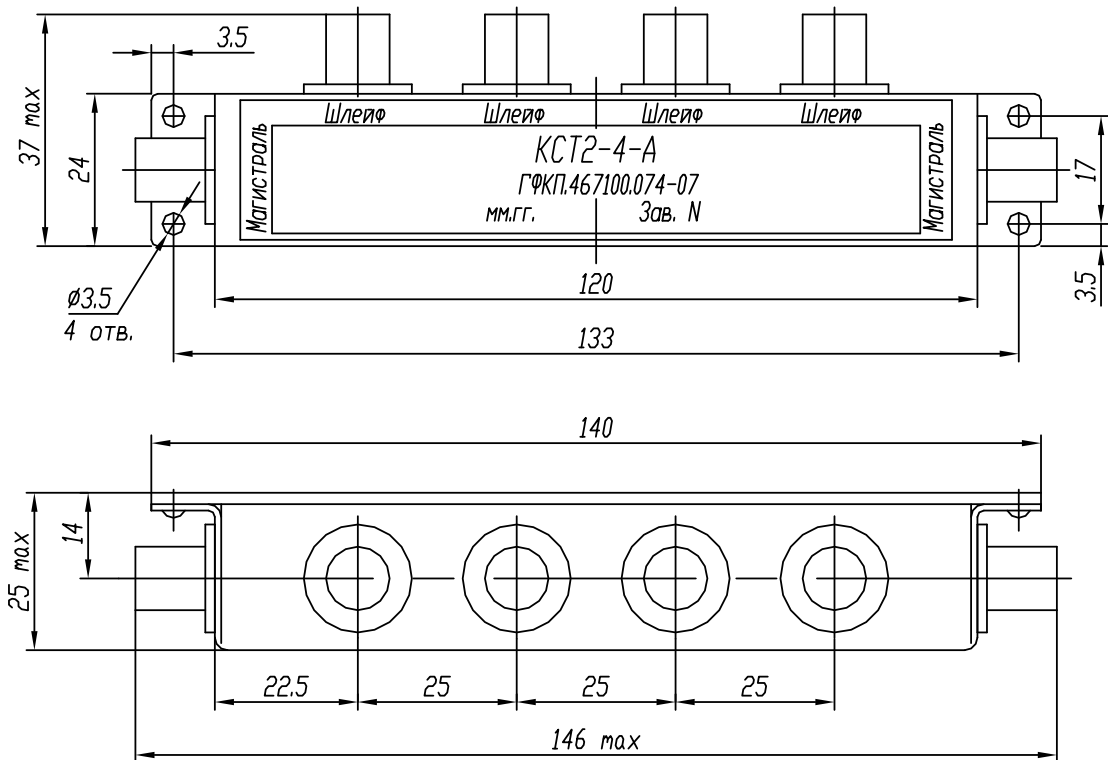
Габаритный чертеж коробки соединительной КСТ2-4
